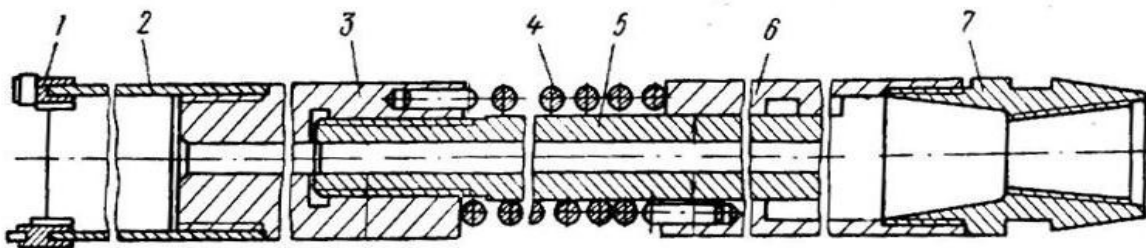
Вібраційно-обертальний колонковий снаряд ВКС-1: 1 – різці; 2 – колонковий снаряд; 3 – обважнювач; 4 – робочі пружини; 5 – стержні; 6 – циліндр; 7 – перехідник
